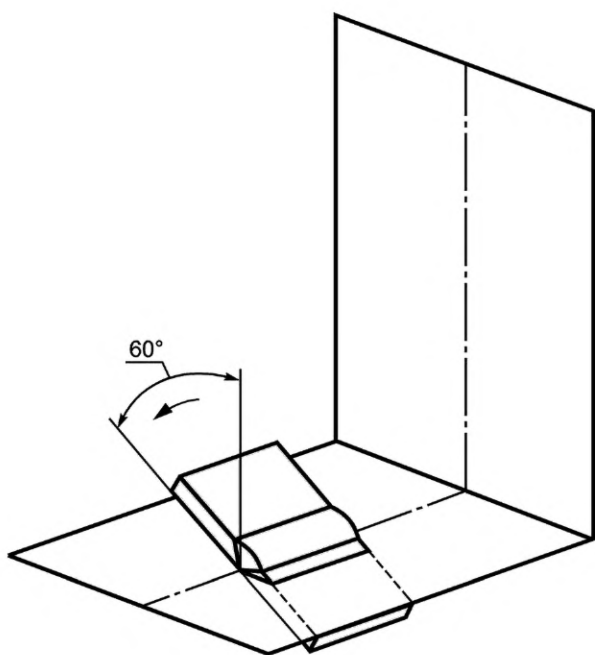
Предельные значения угла наклона и угла поворота для стыковых швов в нижнем положении при сварке РА
